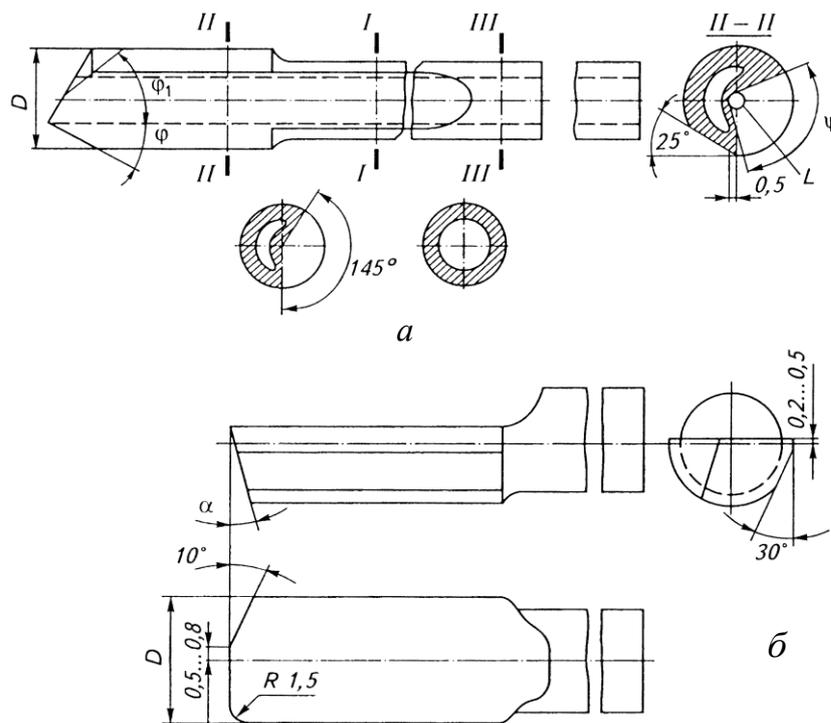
Однолезвийные свёрла для глубоких отверстий:
